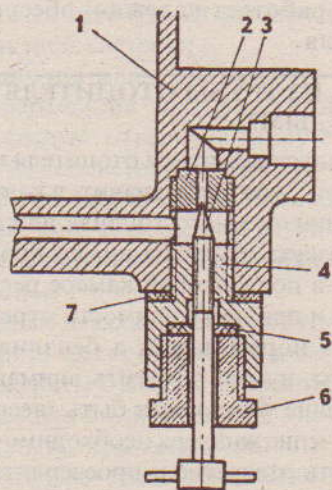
Регулируемый жиклер отопителя: 1 - корпус поплавковой камеры; 2 - жиклер; 3 - регулировочная игла; 4 - корпус; 5 - уплотнение (кожа); 6 - гайка уплотнения; 7 - шайба уплотнительная
